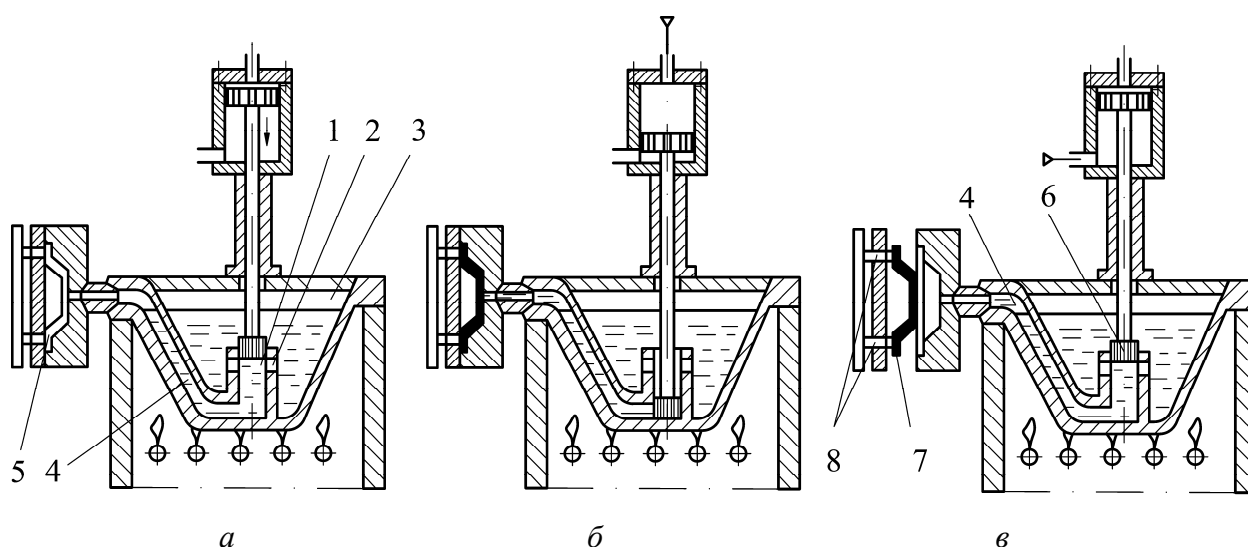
Схема технологического процесса литья под давлением на машине с горячей камерой прессования: а – заполнение камеры прессования расплавом; б – запрессовка; в – раскрытие пресс-формы и выталкивание отливки; 1 – камера прессования; 2 – заливочное отверстие; 3 – тигель с расплавом; 4 – пресс-поршень; 5 – пресс-форма; 6 – пресс-поршень; 7 – отливка; 8 – толкатели
